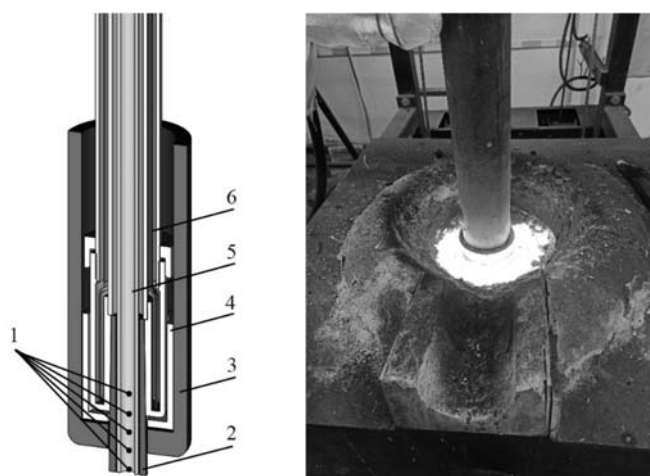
Кристаллизатор установки непрерывного литья вверх и рабочий момент экспериментальной установки
